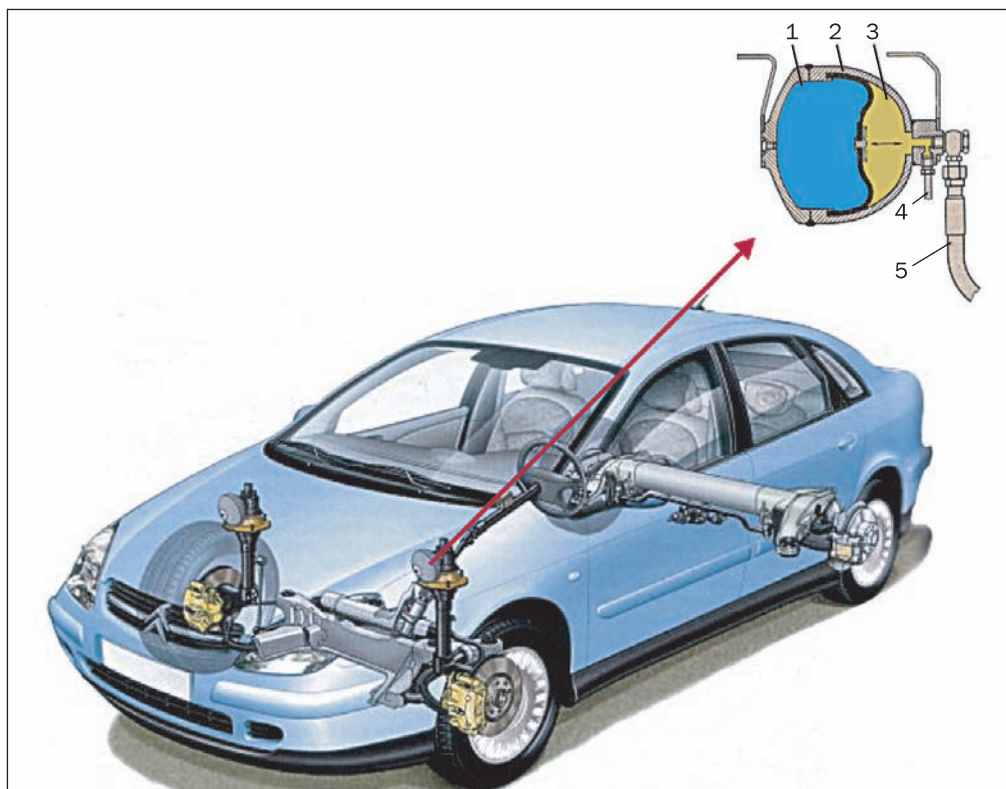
Гидропневматический упругий элемент: 1 — сжатый газ; 2 — корпус; 3 — жидкость; 4 — к насосу; 5 — к амортизаторной стойке
